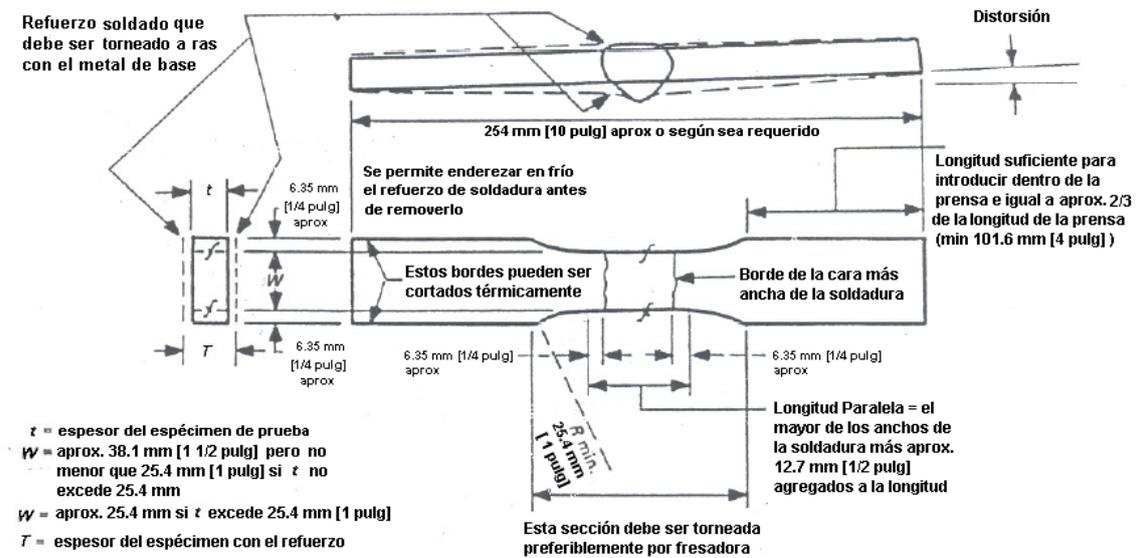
Probeta de acero soldada obtenida de una placa.
